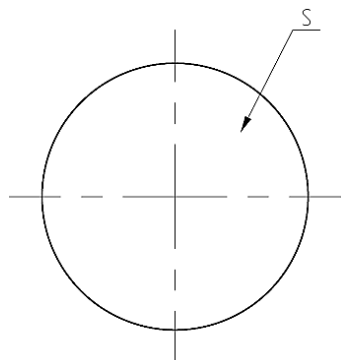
Вид на торец заготовки детали, имеющей площадь S
